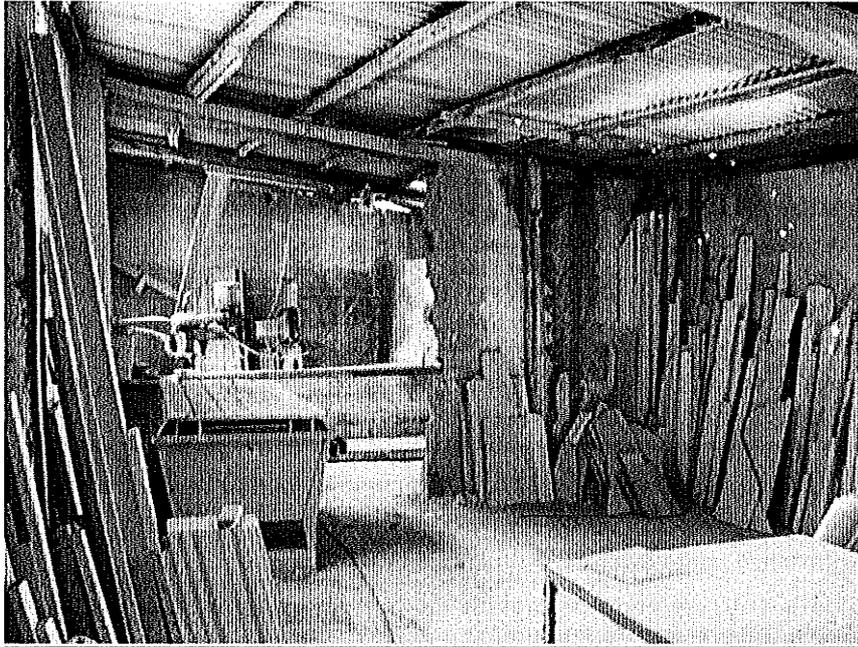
Particolare interno fabbricato A – Zona Lavorazione
